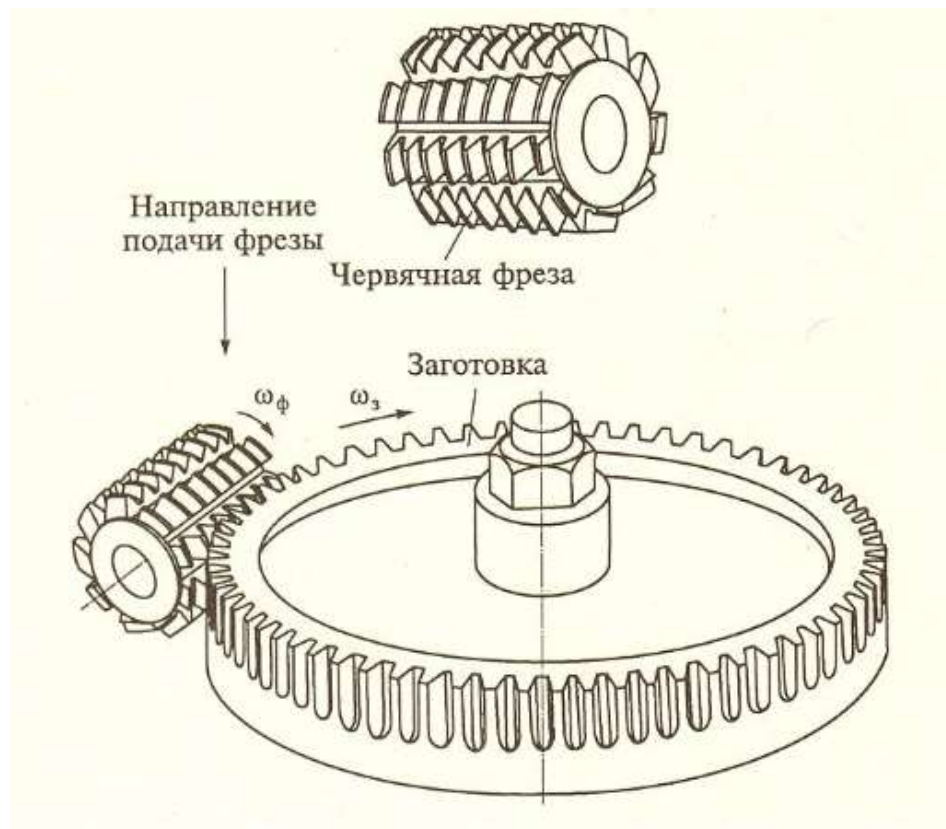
Схеми нарізування зубів методом обкатування черв'ячною фрезой [4]
